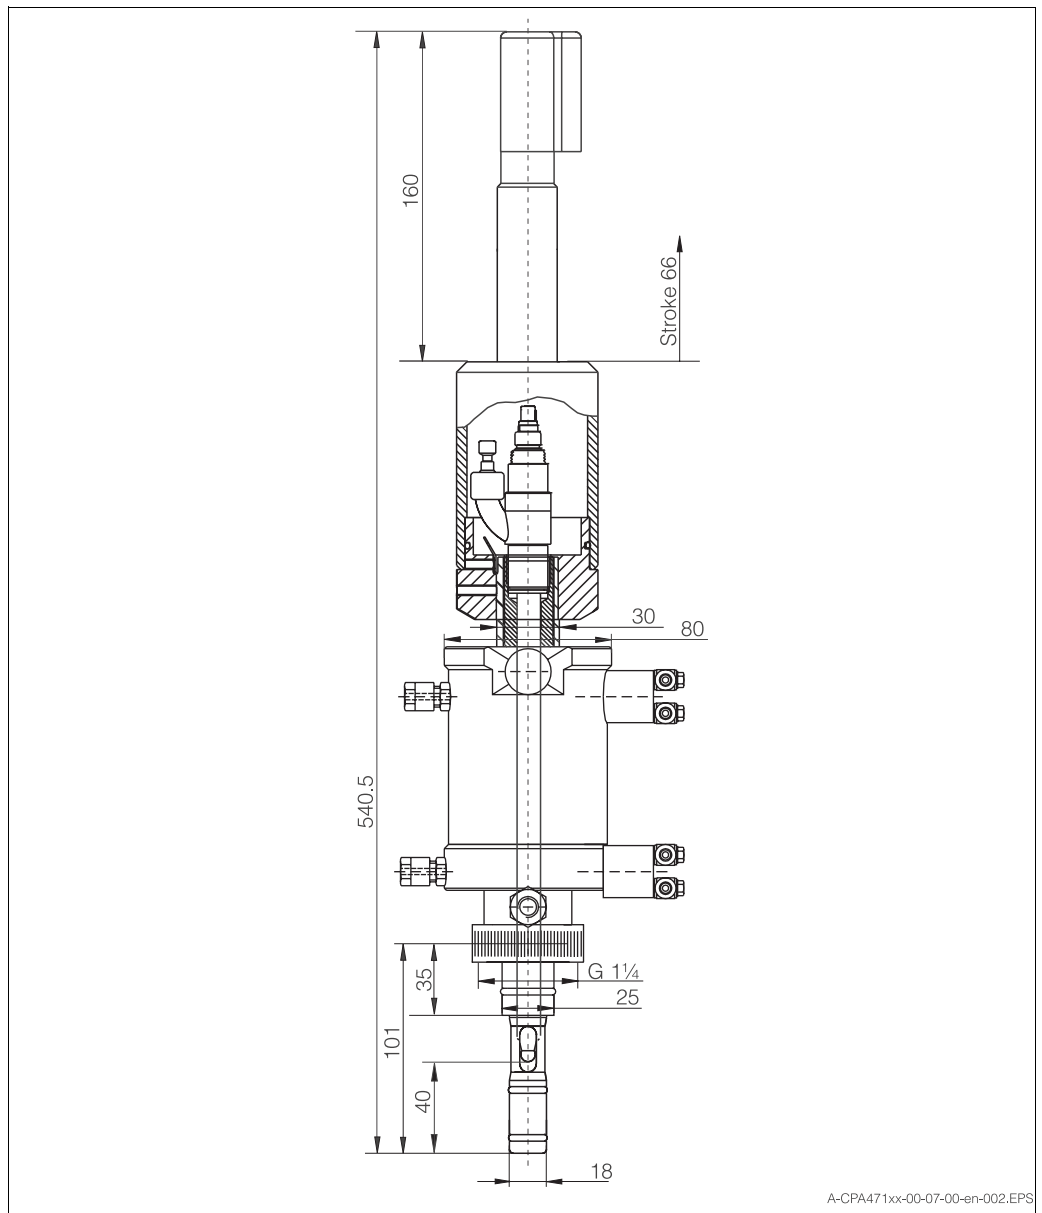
(vlevo): Rozměry CPA 471 - krátké provedení (délka elektrody 120 mm)
